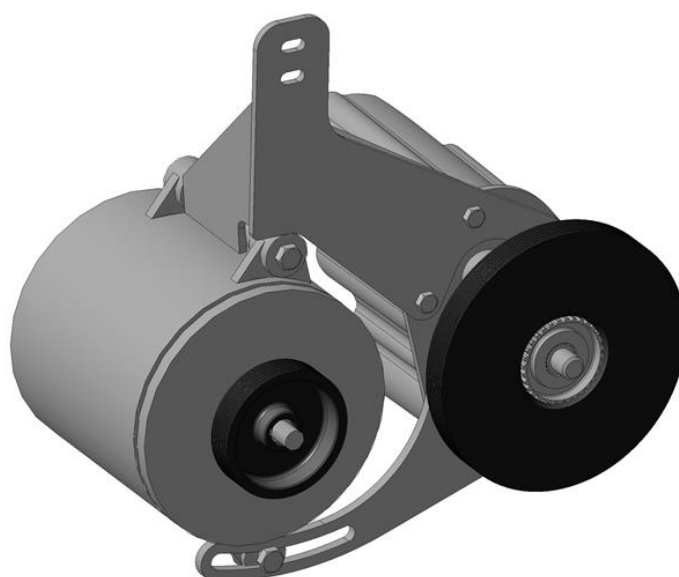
Крепление электродвигателя к коробке передач, шкивы ременной передачи и механизм ее натяжения
